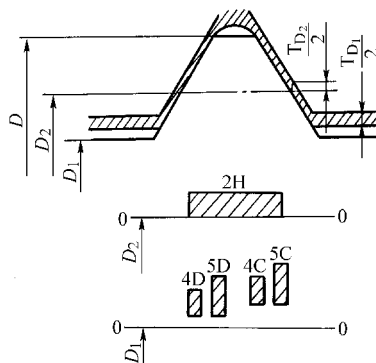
过盈配合螺纹内螺纹公差带
